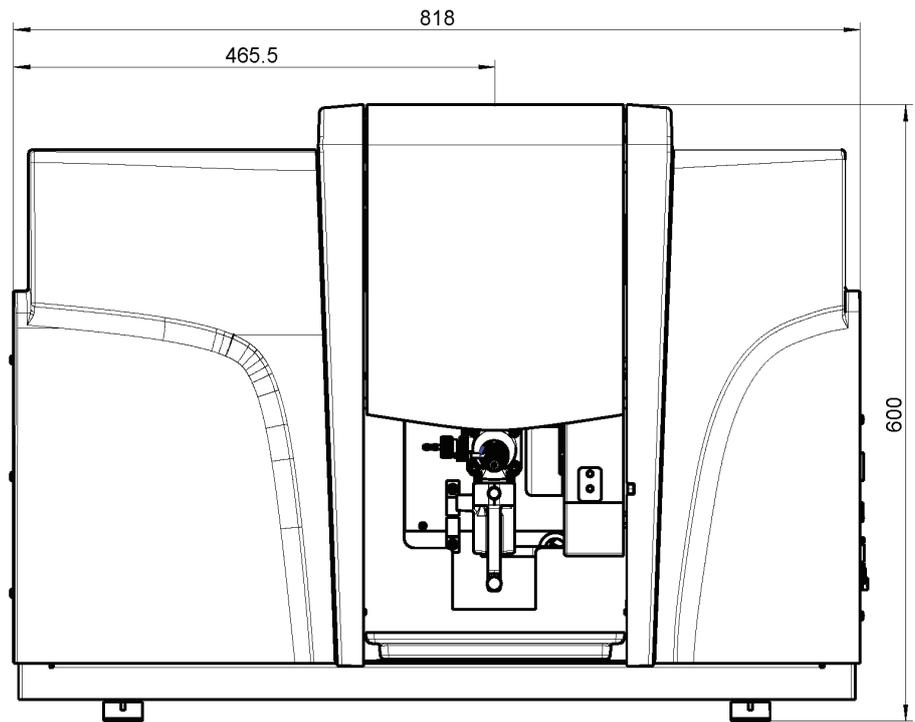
Dimensiones del novAA 800 - Vista frontal
